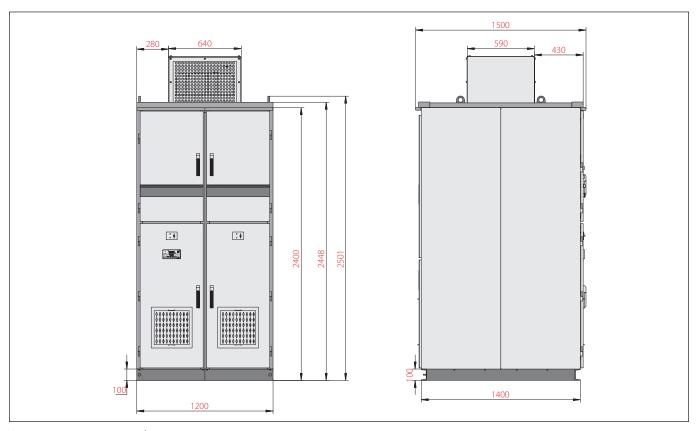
Корпус шкафа токоограничивающего реактора типоразмера ЕА01
